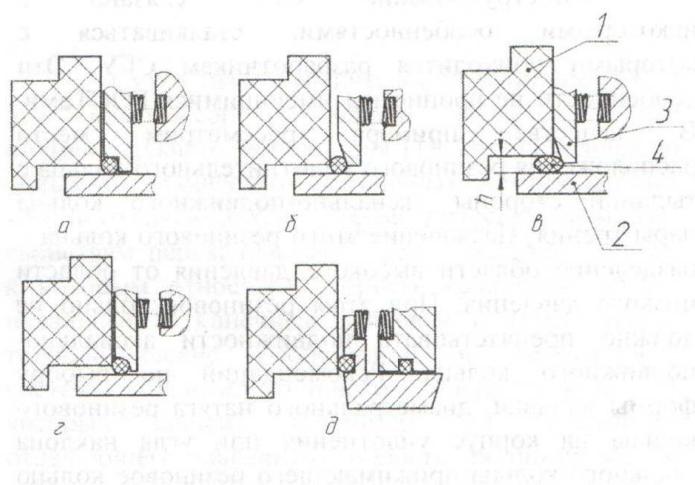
Конструктивное исполнение формы канавки под резиновым уплотнительным кольцом
